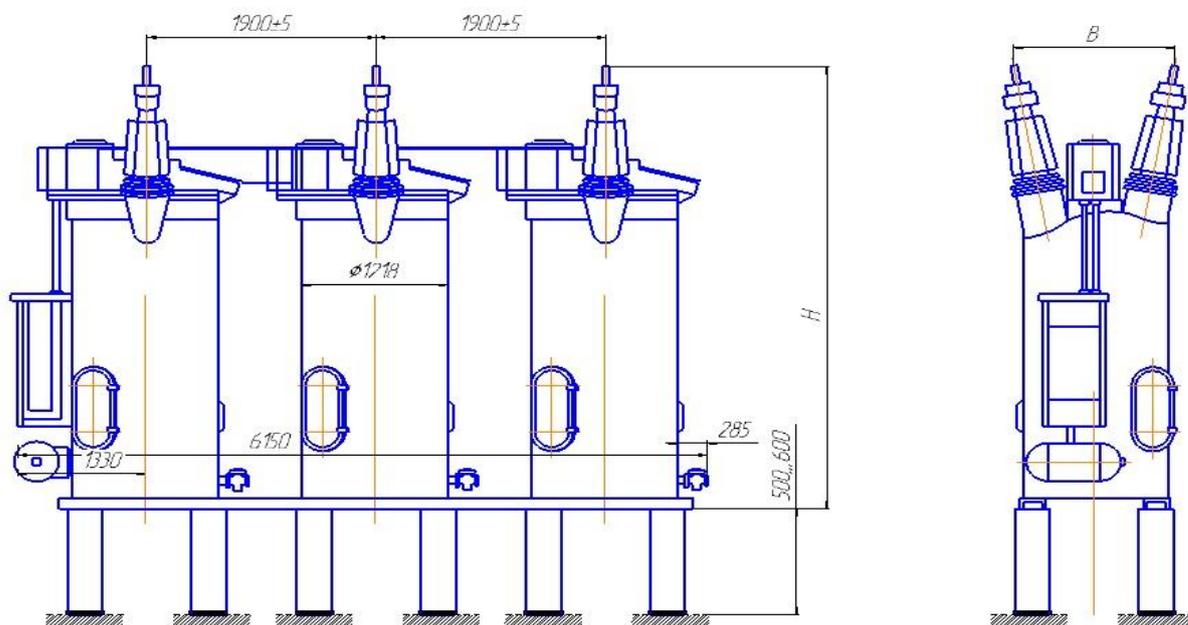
Общий вид, габаритные размеры выключателя У-110-2000-50 У1
